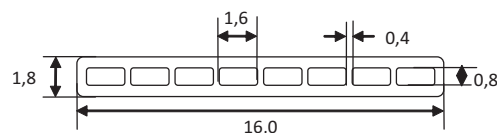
Vue de coupe d'une barrette de mini-canaux (unité : mm)
